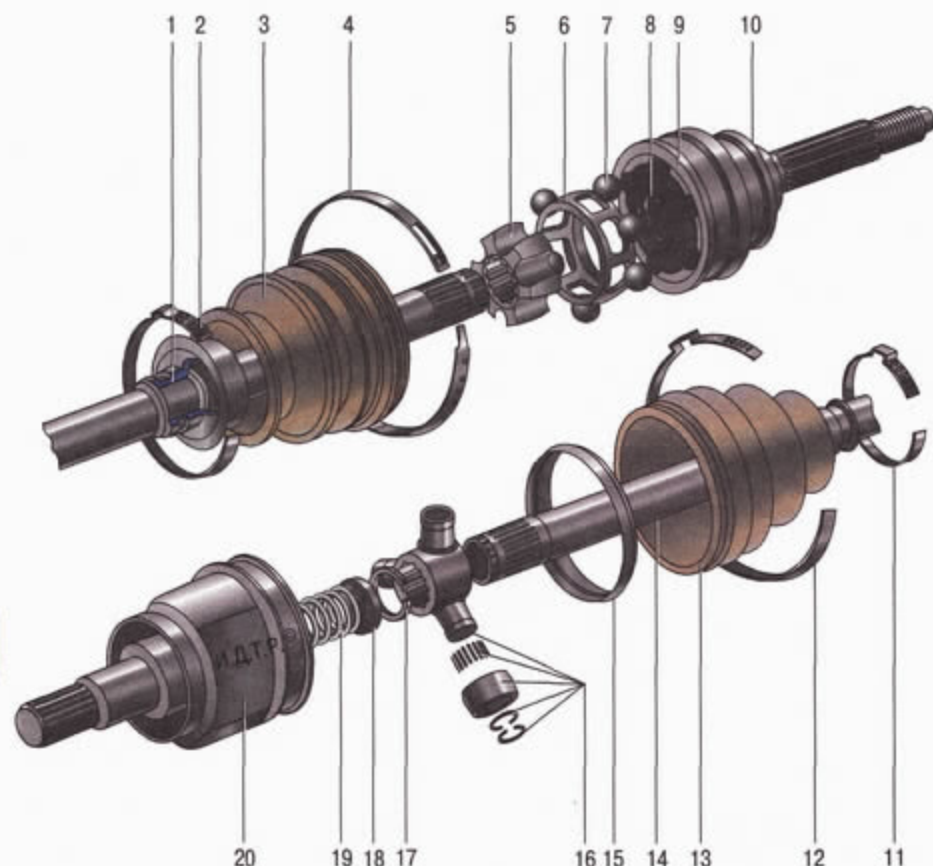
Приводы передних колес: 1 – дренажная втулка; 2 – малый хомут крепления чехла наружного шарнира; 3 – защитный чехол наружного шарнира; 4 – большой хомут крепления чехла наружного шарнира; 5 – обойма; 6 – сепаратор наружного шарнира; 7 – шарик; 8 – стопорное кольцо; 9 – корпус наружного шарнира; 10 – грязеотражатель наружного шарнира; 11 – большой хомут крепления чехла внутреннего шарнира; 12 – малый хомут крепления чехла внутреннего шарнира; 13 – вал шарнирный левый (правый); 14 – защитный чехол внутреннего шарнира; 15 – шайба; 16 – стопорное кольцо; 17 – трехшариковая ступица внутреннего шарнира в сборе с роликами; 18 – чашка пружины; 19 – компенсационная пружина; 20 – корпус внутреннего шарнира
